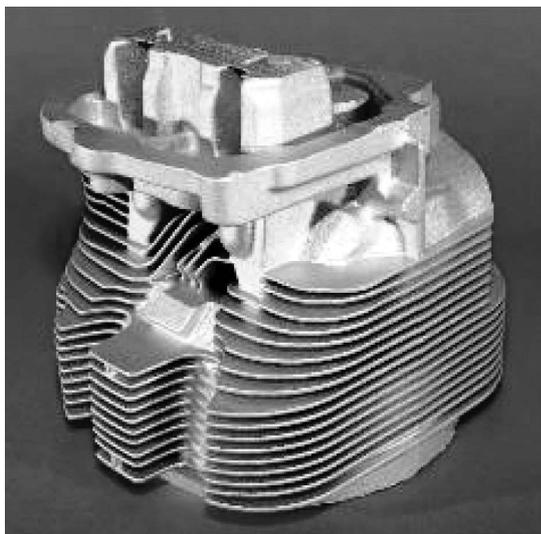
Головка блока цилиндров отлита из сплава Al-8Ce [7]
